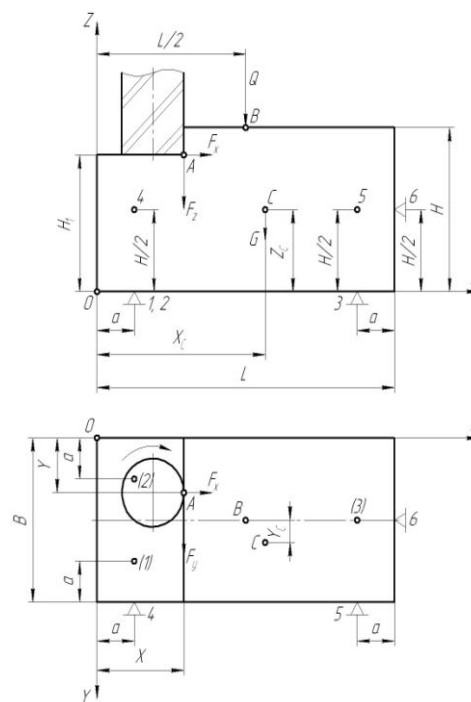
Розрахункова схема механічної системи «верстатний пристрій – заготовка»
